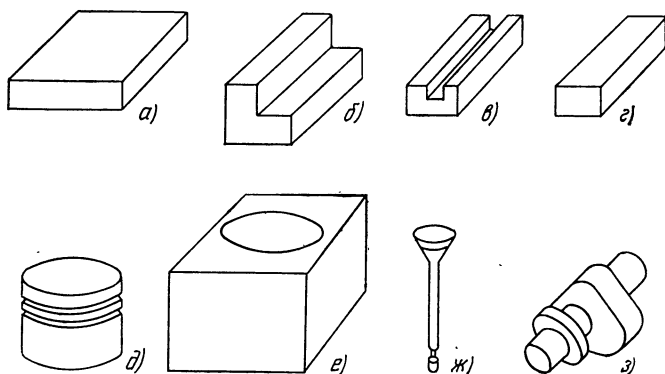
Примеры деталей для лазерной закалки [36]:
